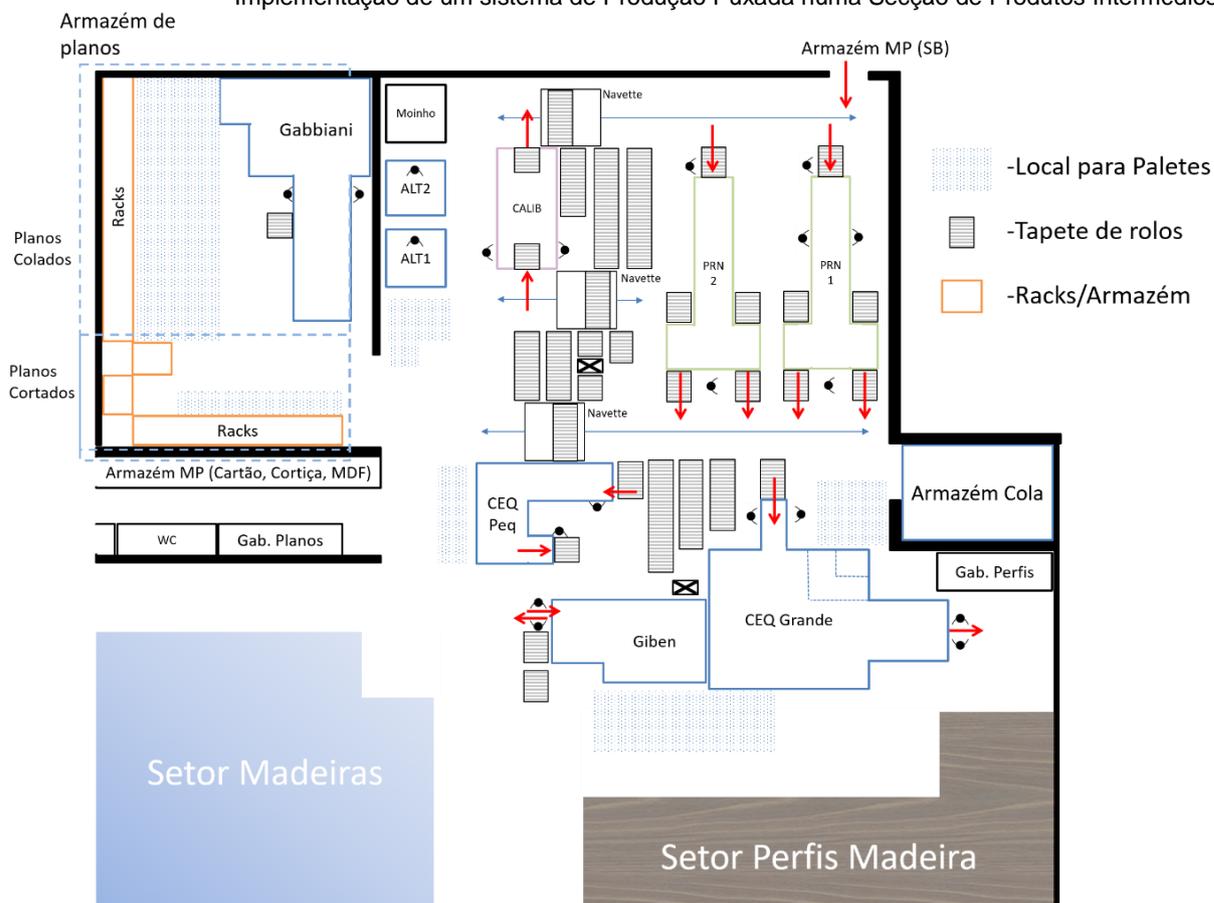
Planta do setor de fabrico de planos e setores vizinhos (Madeiras e Perfis Madeira). Detalhe da planta geral no anexo B.
